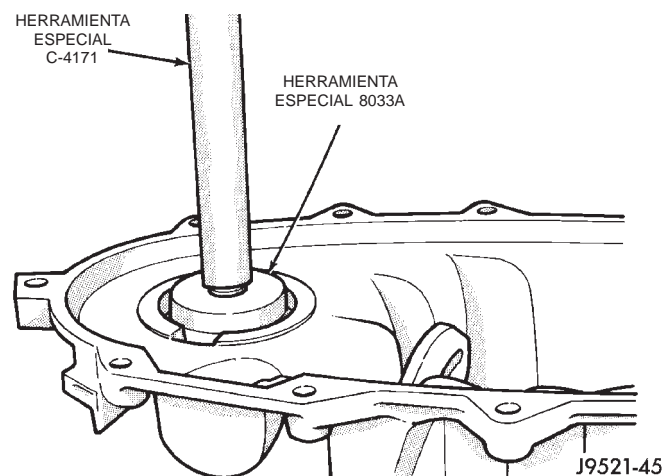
Instalación del cojinete delantero del eje transmisor delantero
